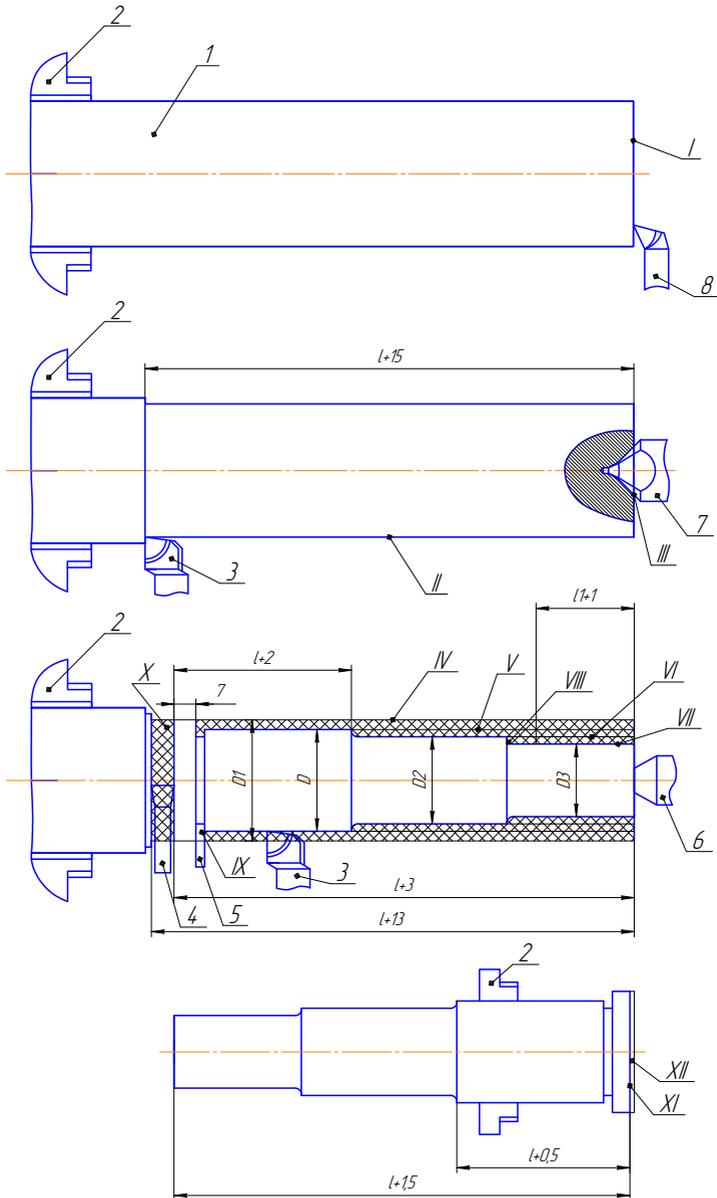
Схема обработки пуансона: 1 – пруток; 2 – патрон; 3 – проходной резец; 4 – отрезной резец; 5 – канавочный резец; 6 – вращающийся центр; 7 – центровочное сверло; 8 – подрезной резец
